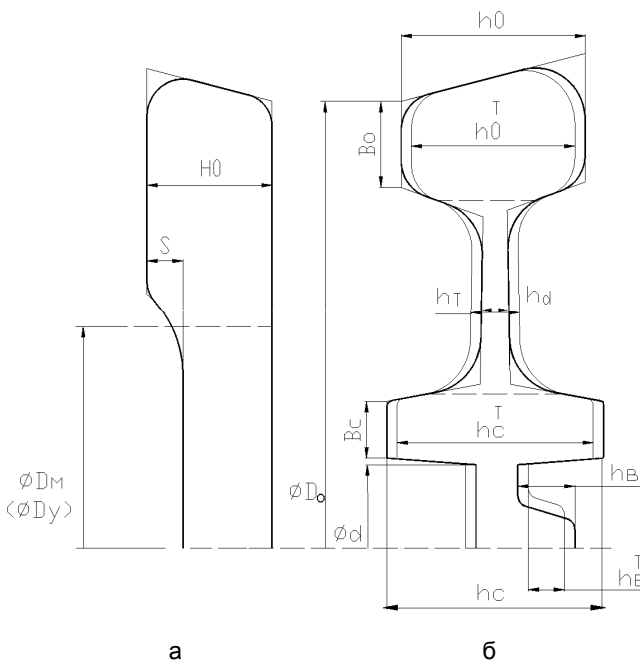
Схема заготовки, получаемой на прессе силой 50 МН (а) и штампуемой из нее на прессе силой 100 МН колесной заготовки (б)
